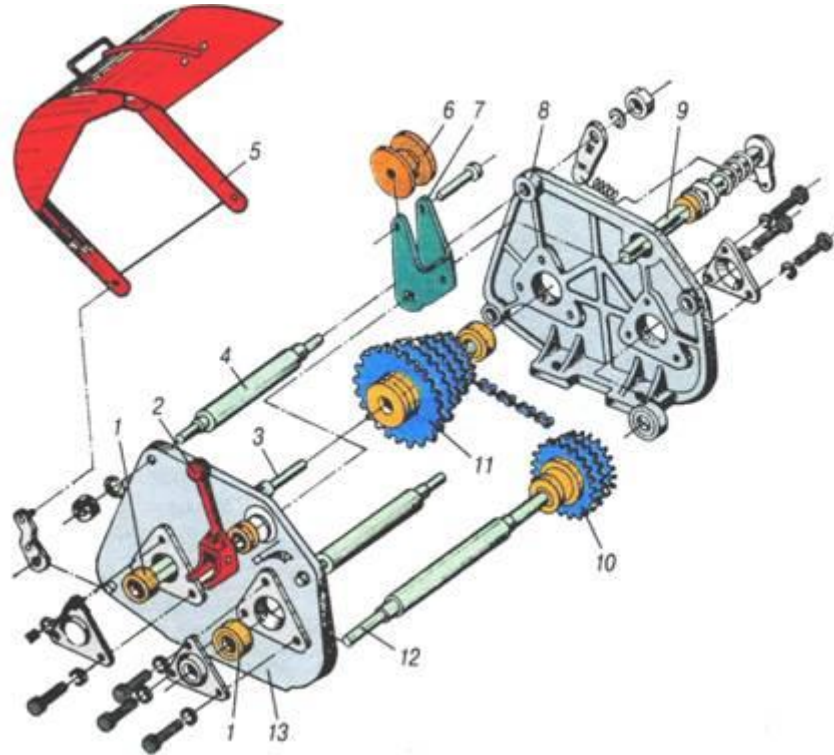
Схема ланцюгового редуктора бурякових сівалок ССТ-12:
